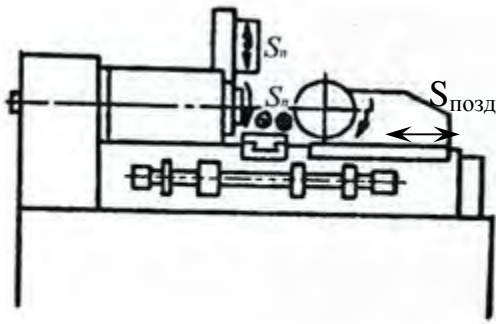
Загальний вид одношпindelного токарно-револьверного автомата
